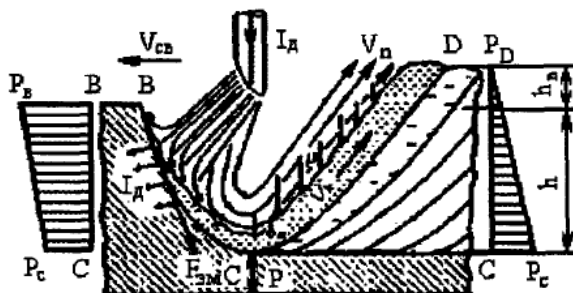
Схема динамічного формування зварювальної ванни
